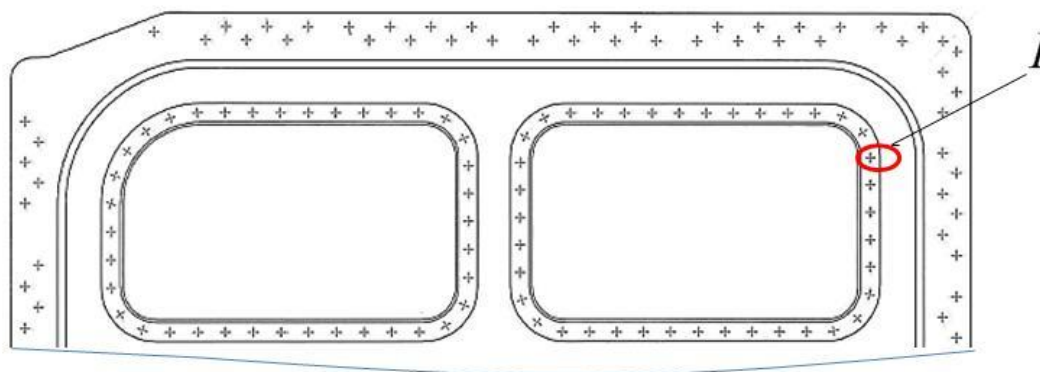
Свариваемый образец № 2: 1 – сварная точка диаметром не более 4,5 мм
